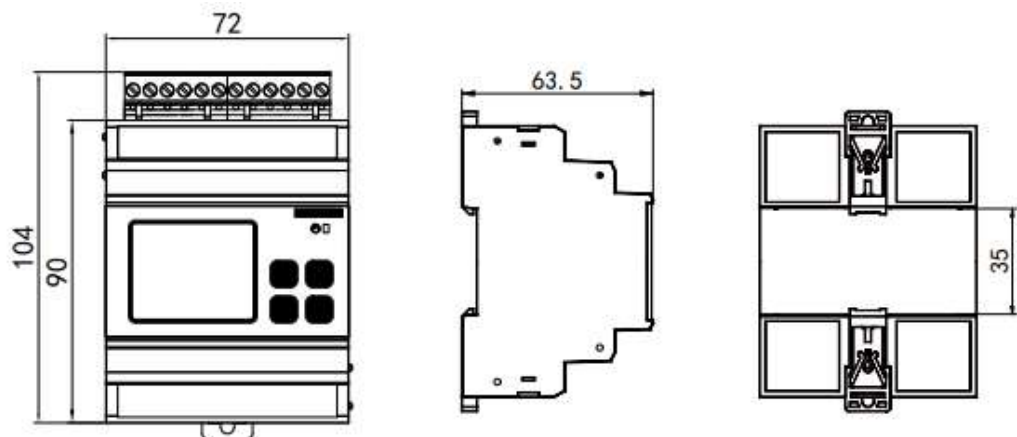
Внешний вид и габаритные размеры модуля измерительного КСМ-М1-1 и КСМ-М1-2
